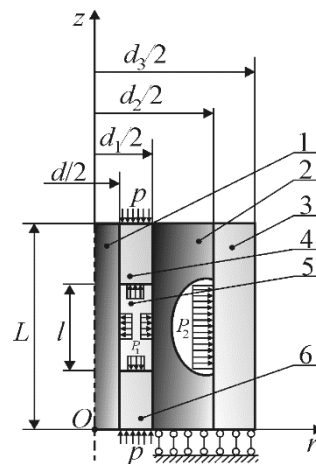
Розрахункова схема прес-форми для виготовлення порожнистих виробів з порошків: 1 – центральний стержень; 2 – вкладиш; 3 – матриця; 4, 6 – пуансон; 5 – брикет з порошку
